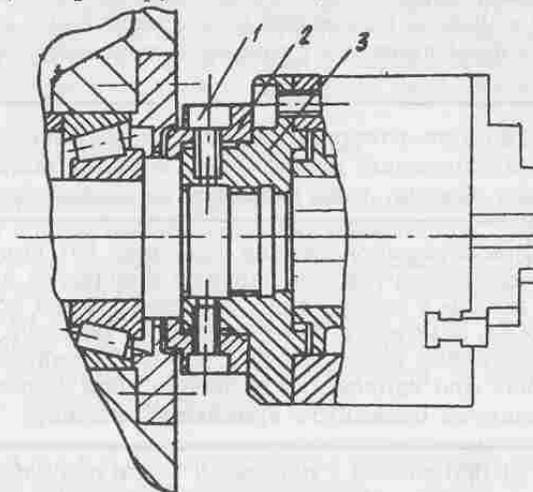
Трехкулачковый патрон на шпинделе станка.
